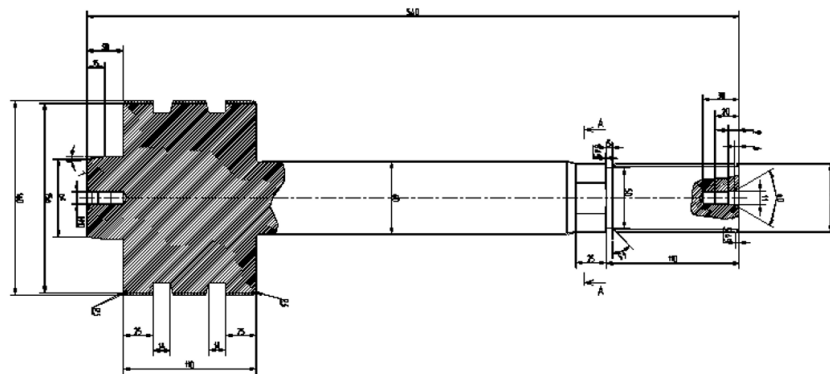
Общий вид поршня цилиндра мельницы валовой
